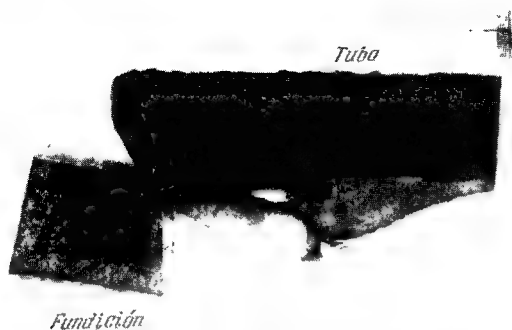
En la sección de la junta soldada que une el tubo con la fundición derecha se ven las soldaduras defectuosas (aproximadamente en  $1/3$  de la magnitud).
